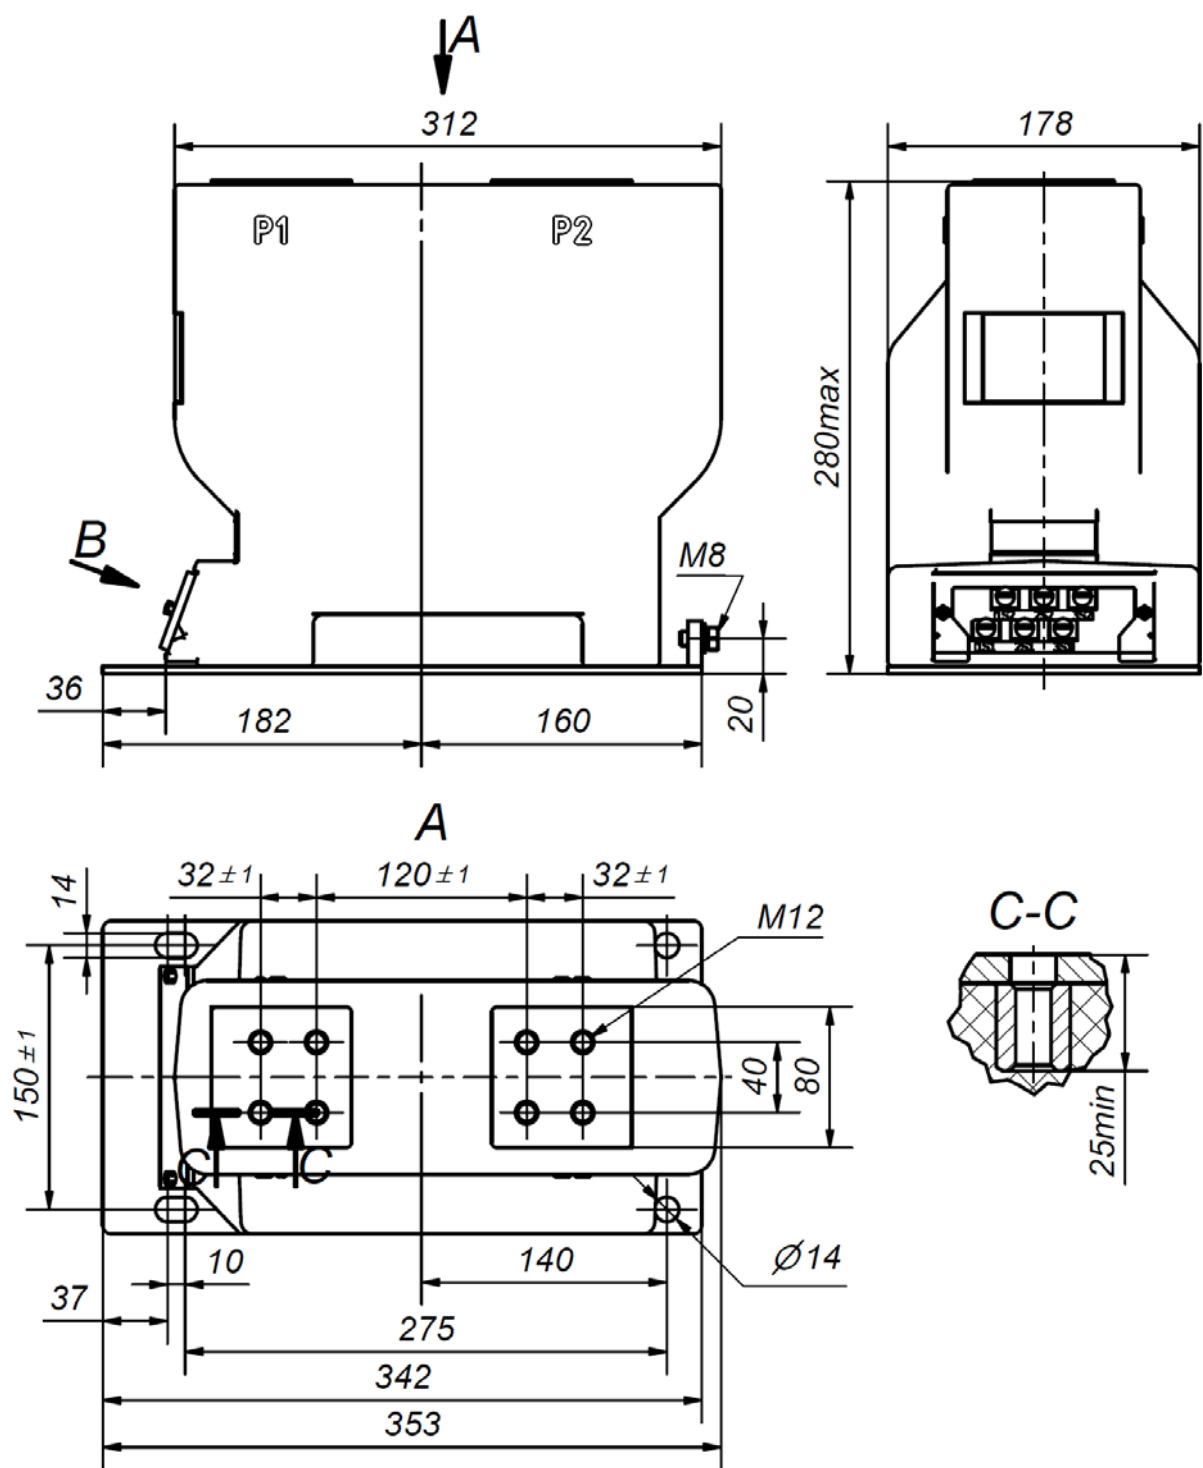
Габаритный чертеж трансформаторов TCS1-12-22.XX.2...
